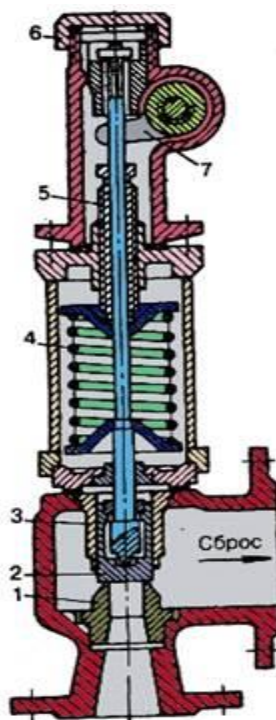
Предохранительный сбросной клапан типа ППК – 4. 1 – седло клапана; 2 – золотник клапана; 3 – сопло клапана; 4 – пружина; 5 – регулировочная втулка; 6 – разделительная перегородка; 7 – рычажный механизм.
